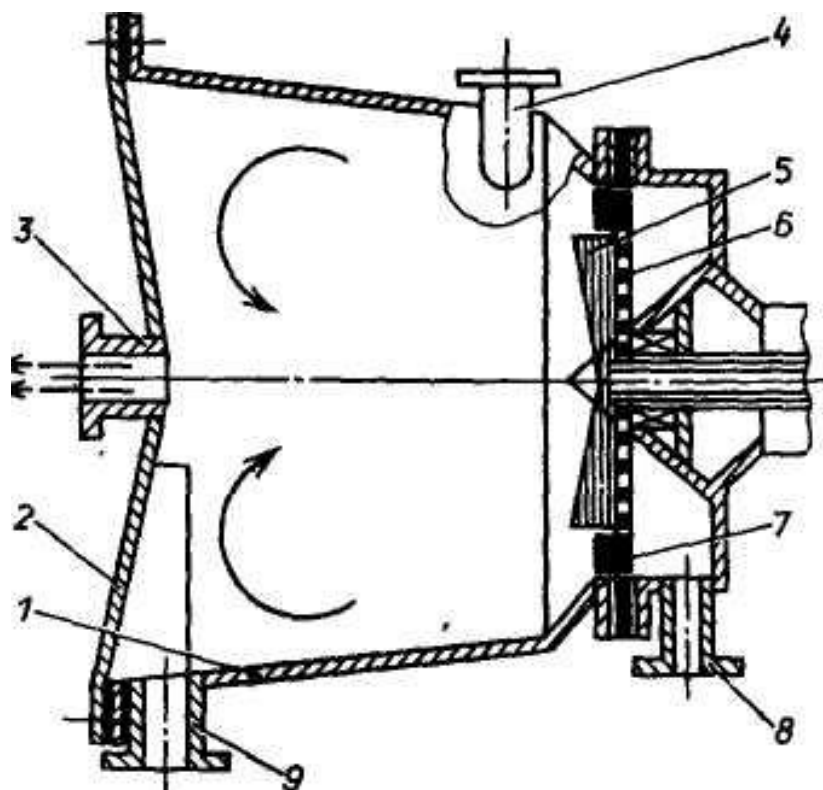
Схема гидроразбивателя Фиберизер: 1 — емкость; 2 — крышка; 3 — патрубок отвода легких отходов; 4 — патрубок подачи массы; 5 — ротор; 6 — сито; 7 — статор; 8 — патрубок отвода готовой массы; 9 — патрубок отвода тяжелых загрязнений
